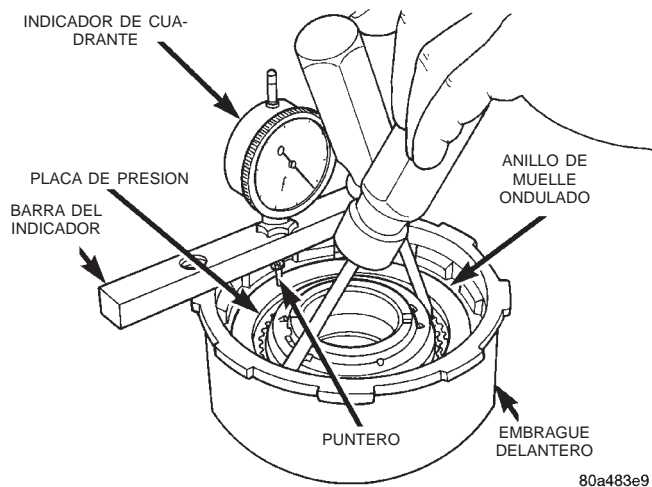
Medición de la holgura del conjunto de embrague delantero
